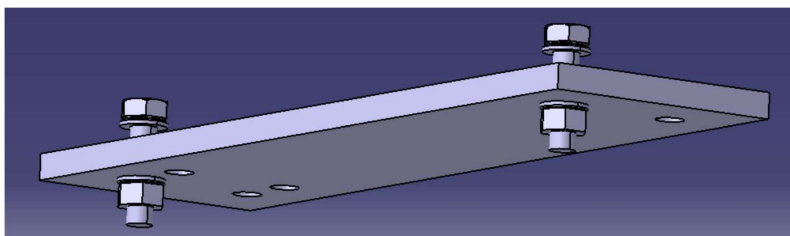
Placa de la unión tipo 1 vinculada con las primeras piezas del conjunto
